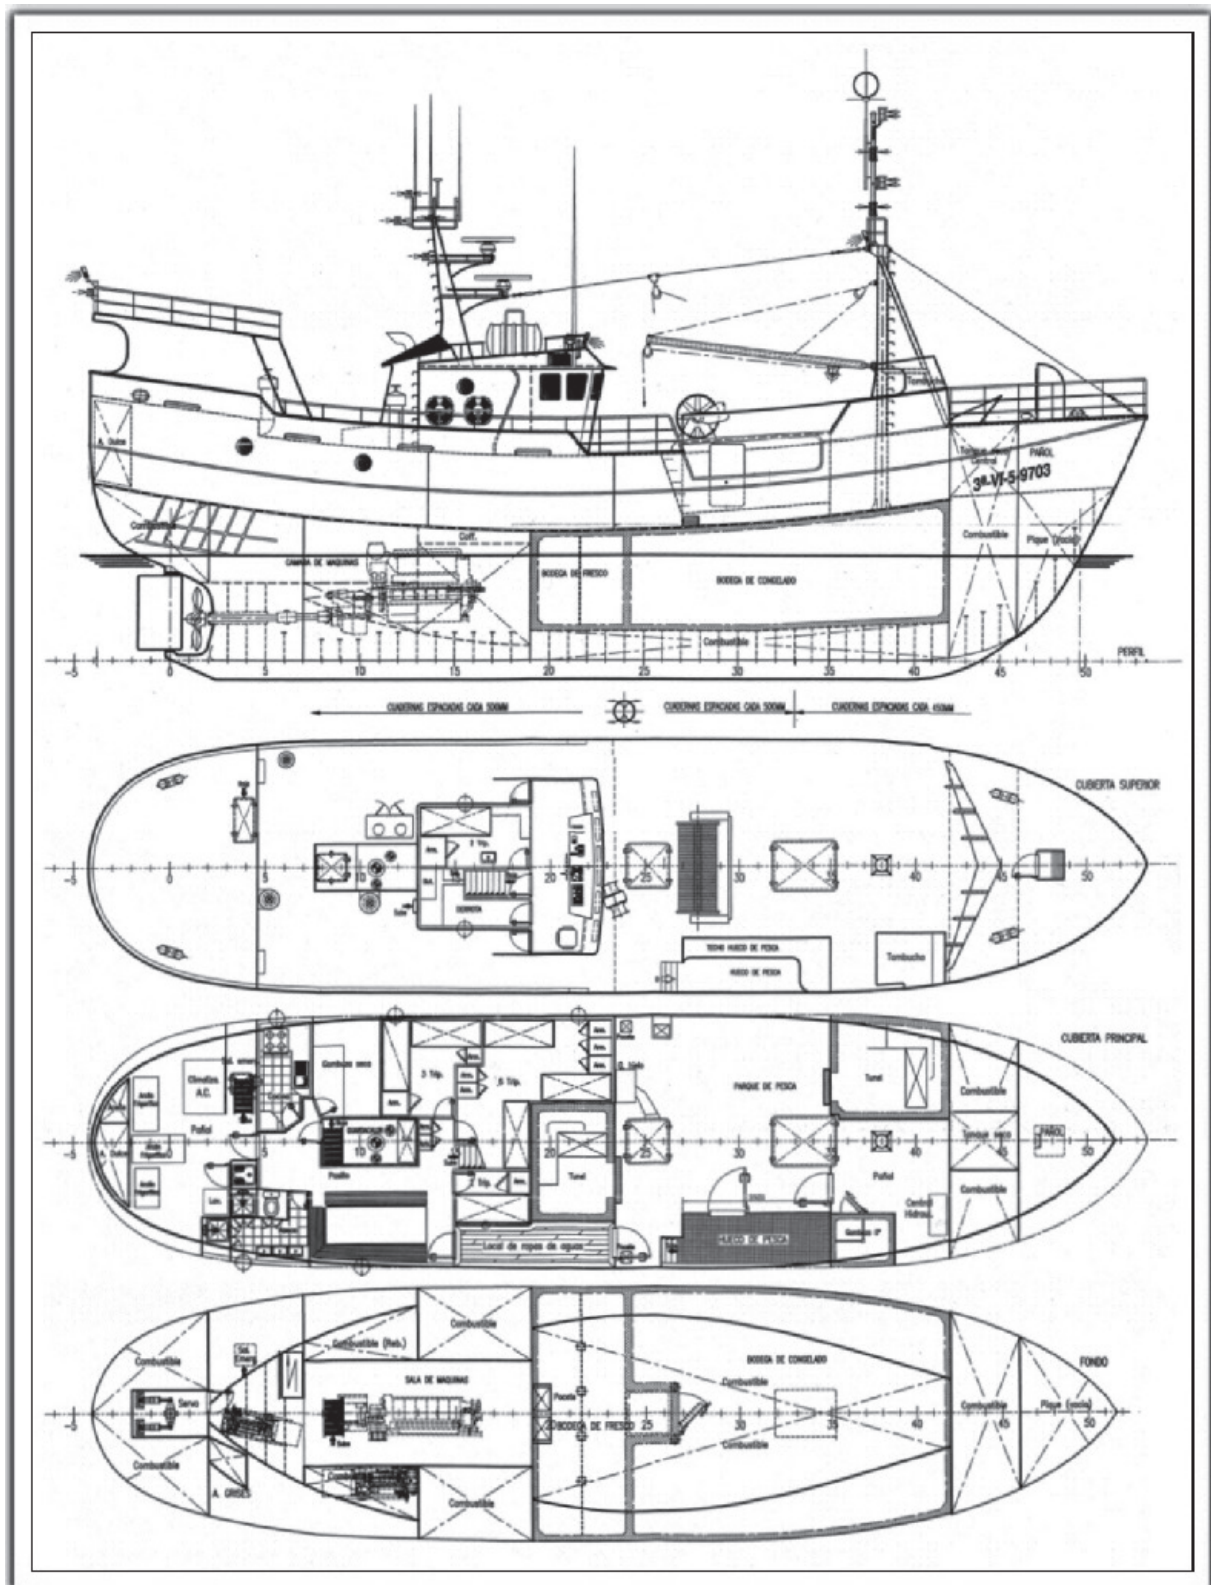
Plano de disposición general del buque tras las modificaciones realizadas
